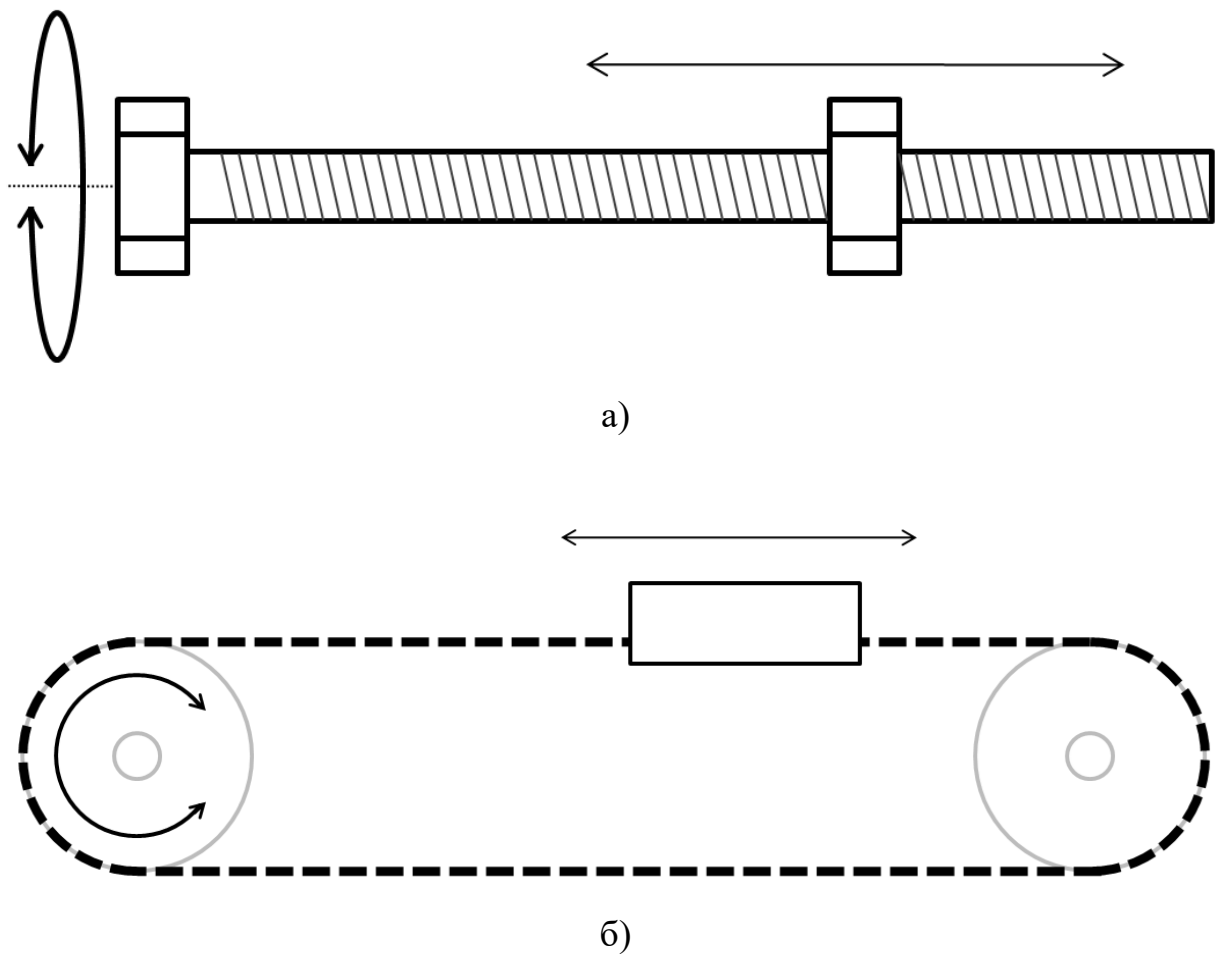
Лінійні напрямні: а - привід зі шпинделем; б - ремінний привід
